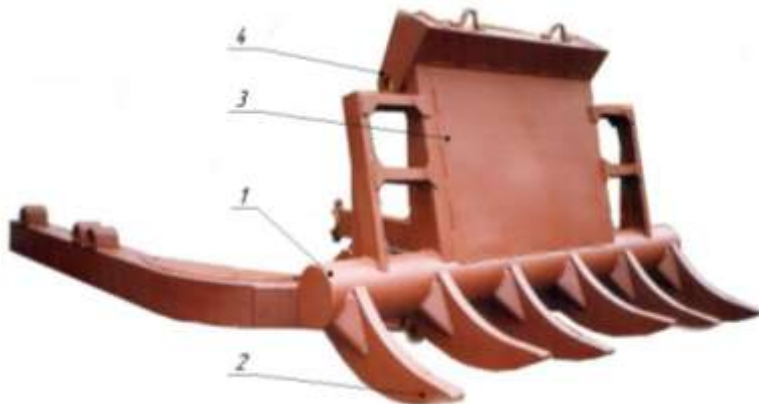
Орган корчевальный в сборе с рамой универсальной:
